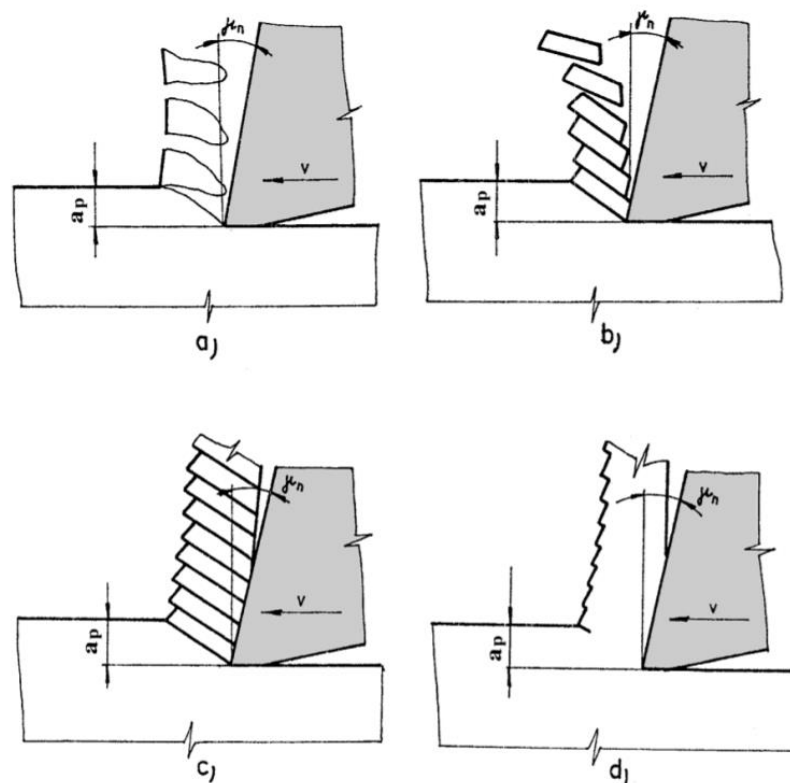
Základní druhy vznikajících třísek při obrábění kovů [31]
